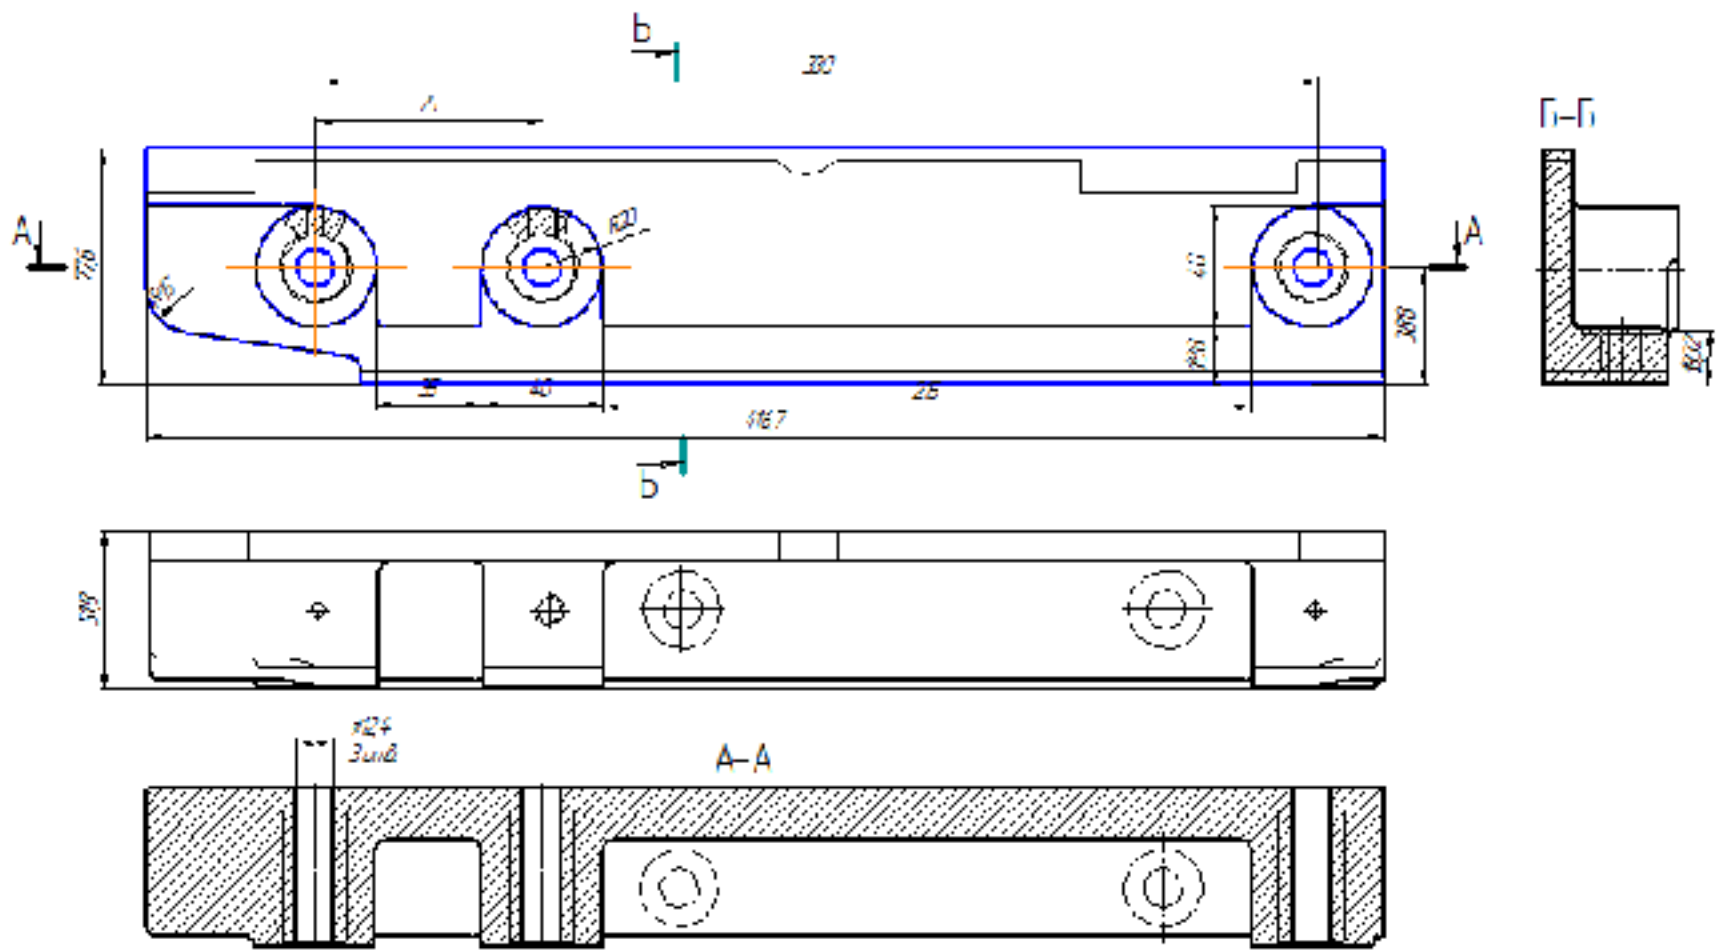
Ескіз заготовки при литті в піщано-глинисті форми
